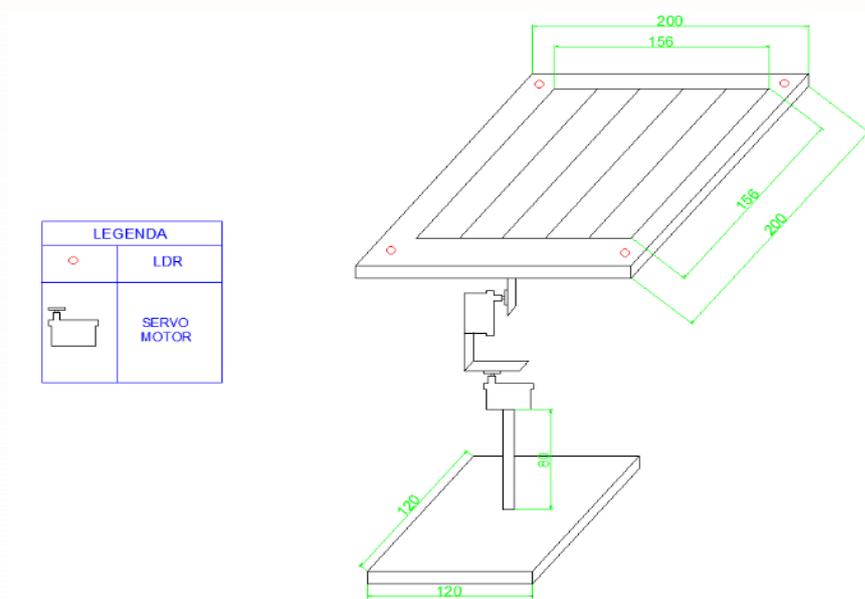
Layout do projeto (Fonte: Autoria própria)
